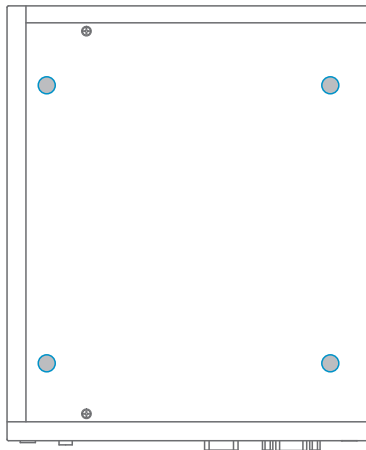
Maßzeichnung Profile Unit Controller mit Montageadapter
